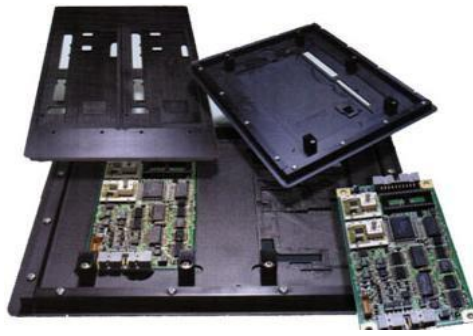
5 Produk *Precision Machining jig and Fixture
